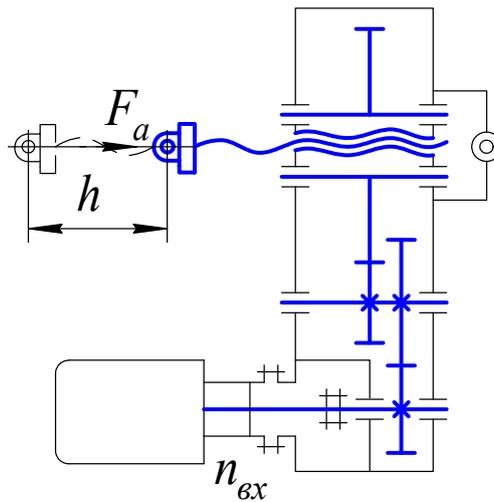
Схема редуктора, выполненного по развернутой схеме
